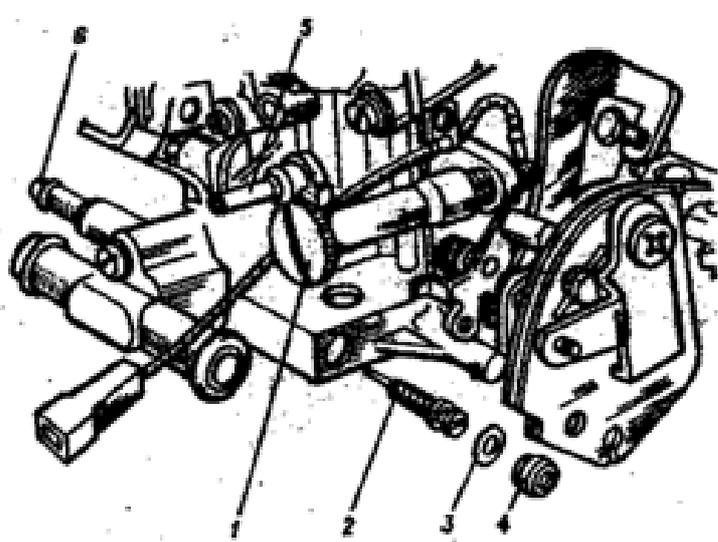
Винты регулировки системы холостого хода карбюратора: 1 - регулировочный винт количества смеси; 2 - регулировочный винт качества (состава) смеси; 3 - уплотнительное кольцо; 4 - заглушка регулировочного винта; 5 - штуцер к вакуум-корректору датчика-распределителя зажигания; 6 - штуцер отсоса картерных газов в смесительную камеру
